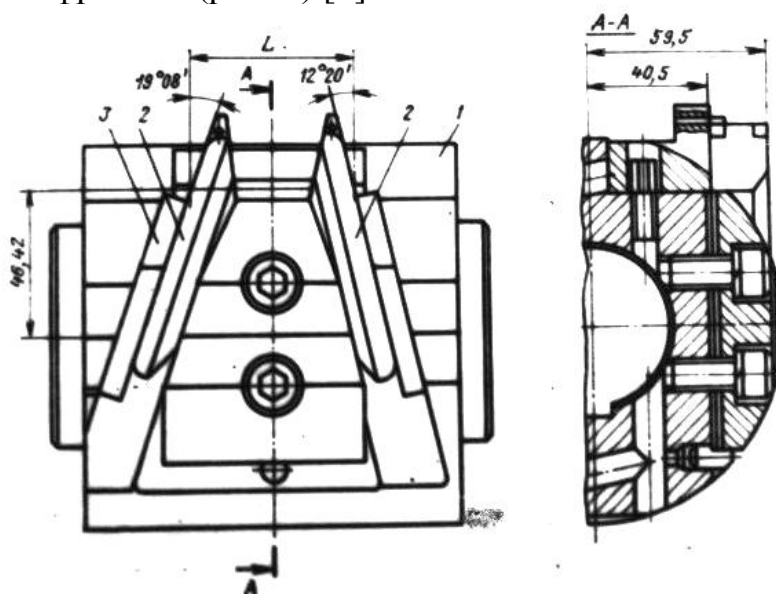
Обкаточный двухкромочный твердосплавный резец конструкции ЦНИИТМАШ $m=12$ мм.
